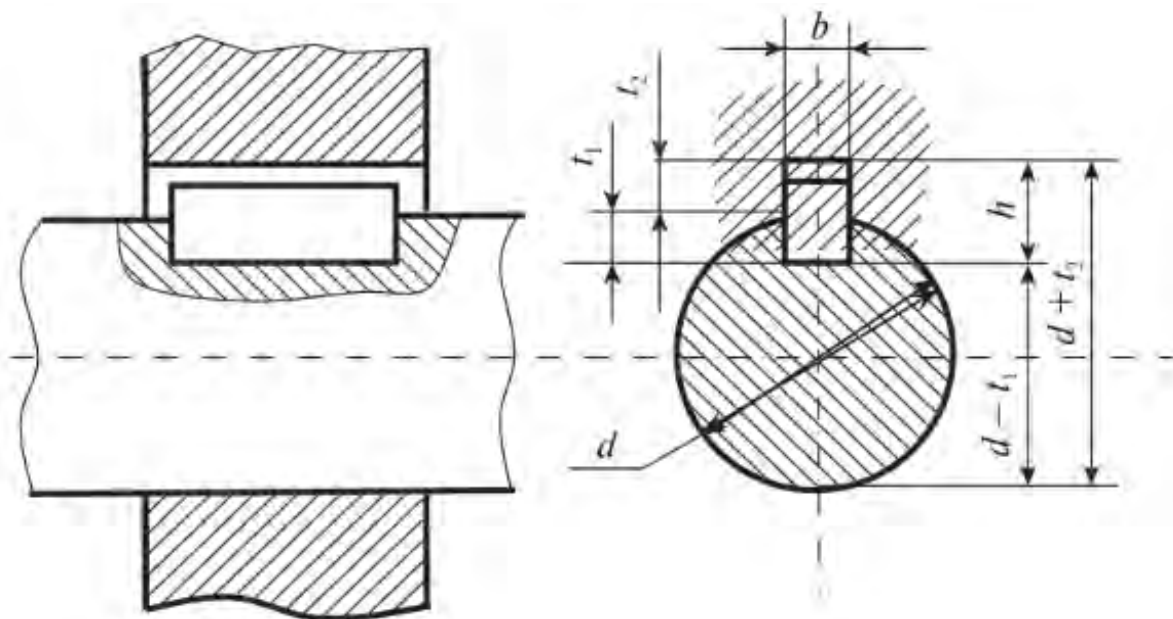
Схема шпоночного соединения с призматической шпонкой:
